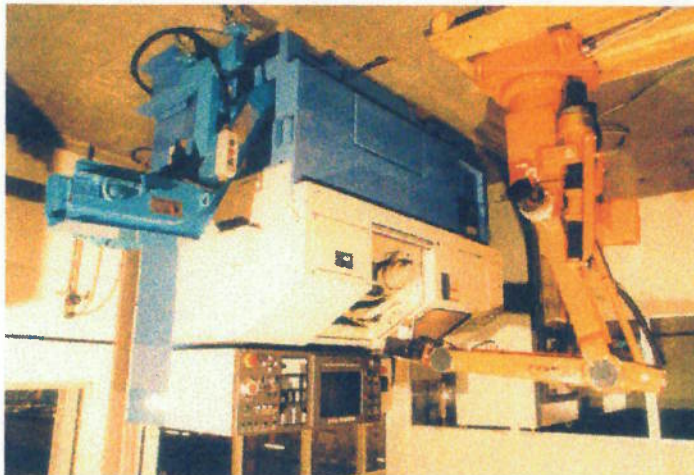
Sistema de manufatura composto por um Robô e uma máquina CNC.
